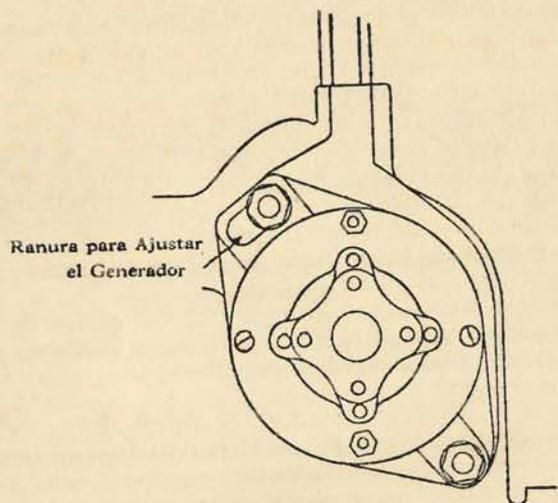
La Cadena se Ajusta Cambiando la Posición del Generador
